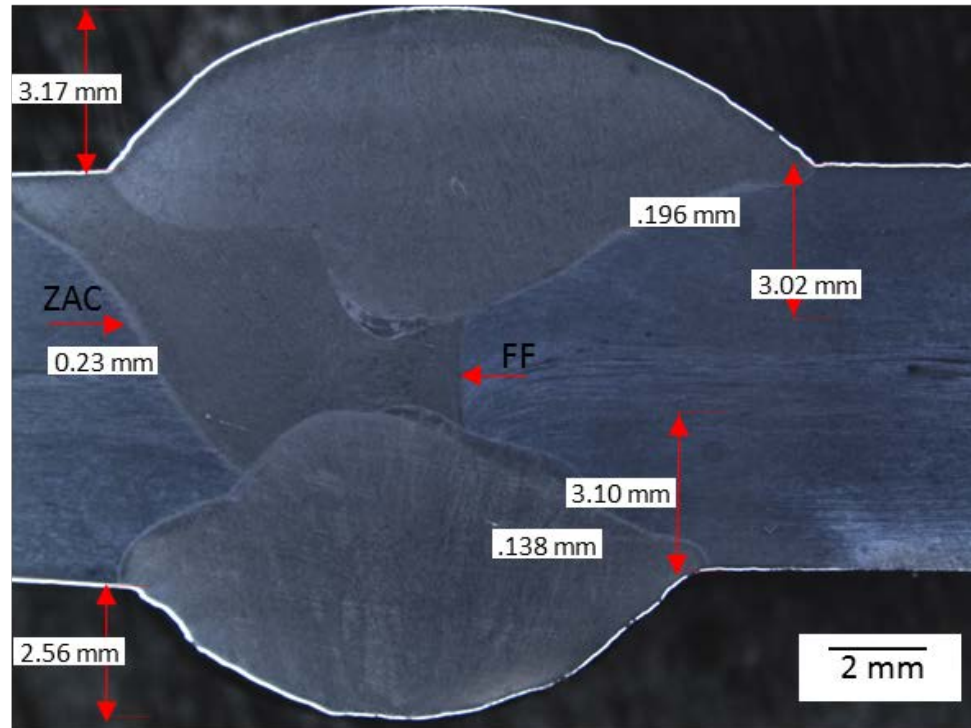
Imagen por macrografía óptica de la soldadura mostrando las características dimensionales y puntualizando la zona afectada de calor (ZAC) y la discontinuidad de falta de fusión (FF).
